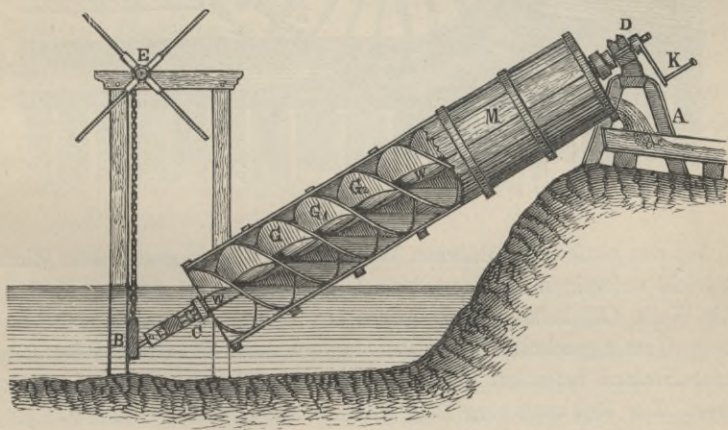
Ummantelte Wasserschnecke oder Tonnenmühle.
